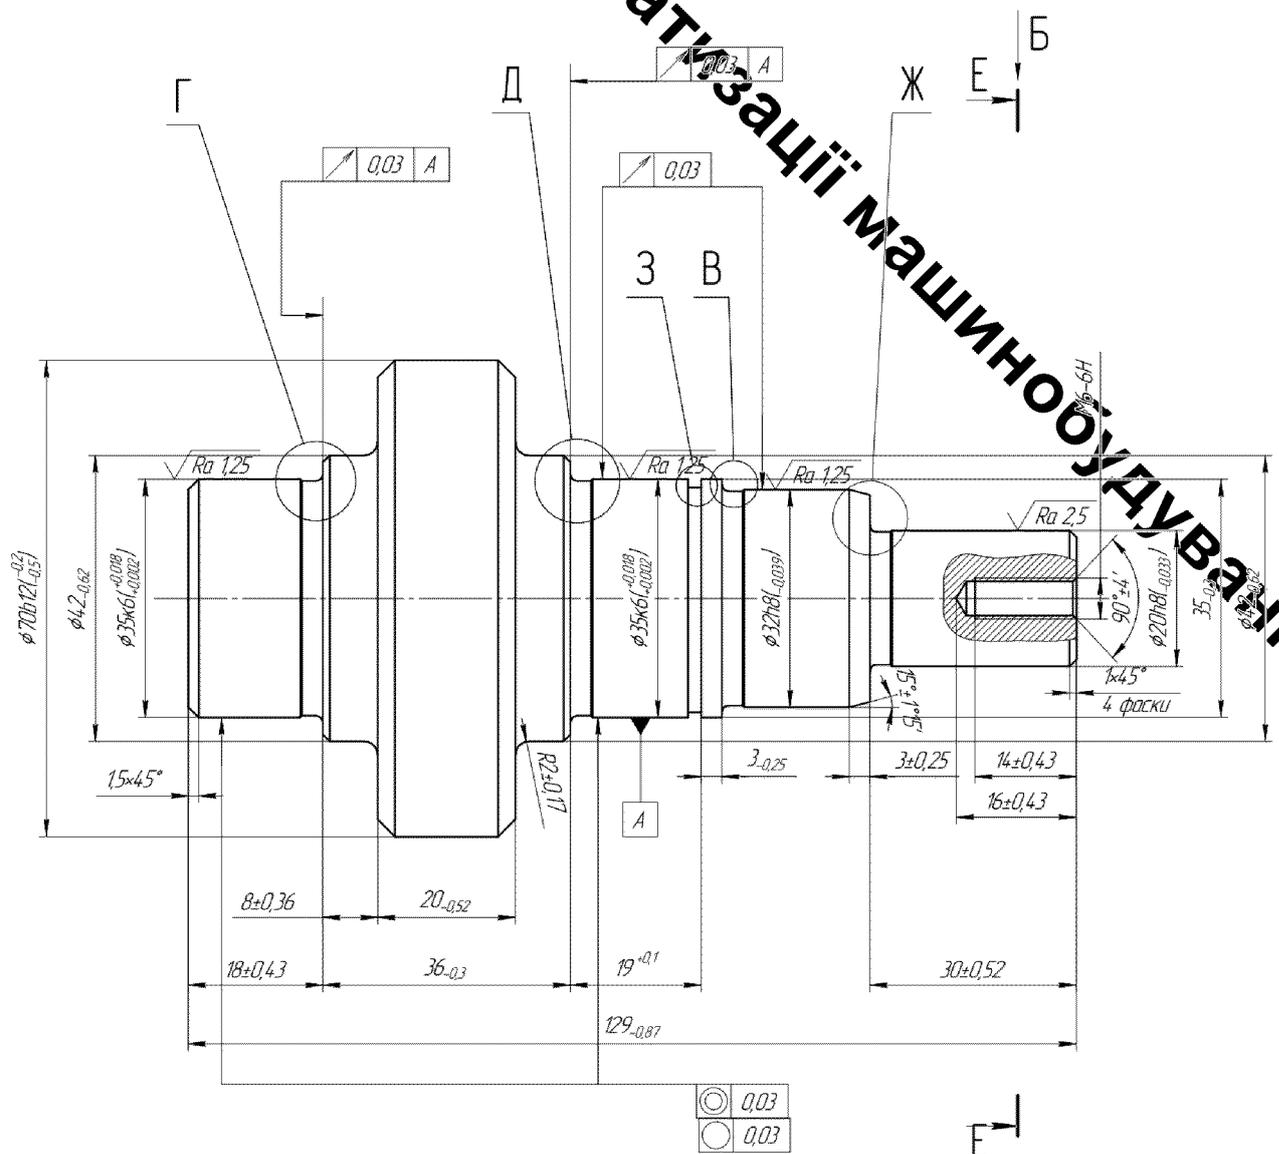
Кресленник деталі «Вал-шестерня Д02210.5»
